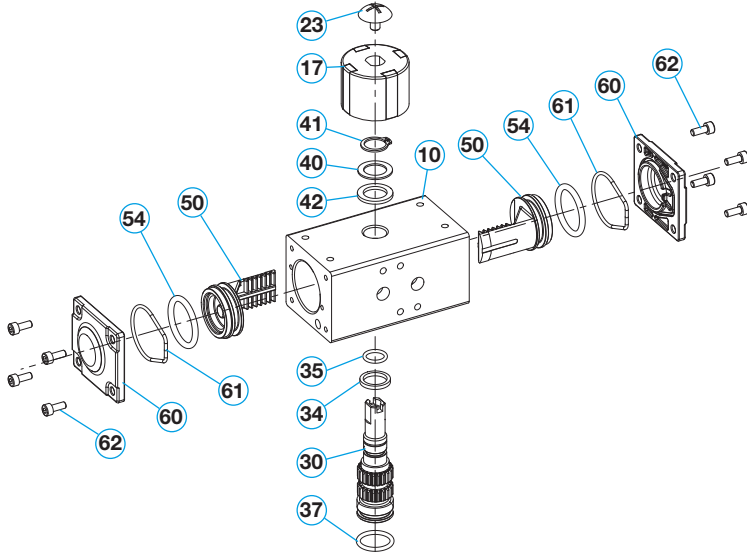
Explosionszeichnung aller Einzelkomponenten Schwenkantrieb bar-agturn
